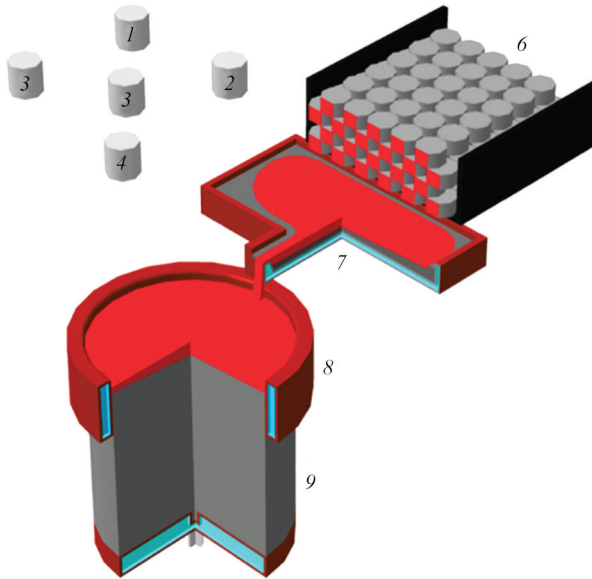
Схема електронно-променевої плавки з проміжною ємністю: 1–5 — електронно-променеві гармати; 6 — витратна заготовка; 7 — проміжна ємність; 8 — кристалізатор; 9 — зливко, що виплавляється
